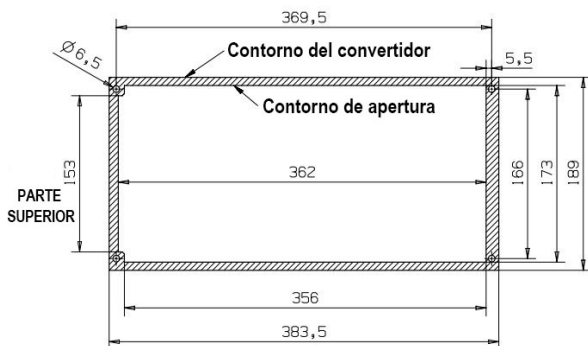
Dimensiones de corte del montaje con bridas para M14 (Unidad: mm)
